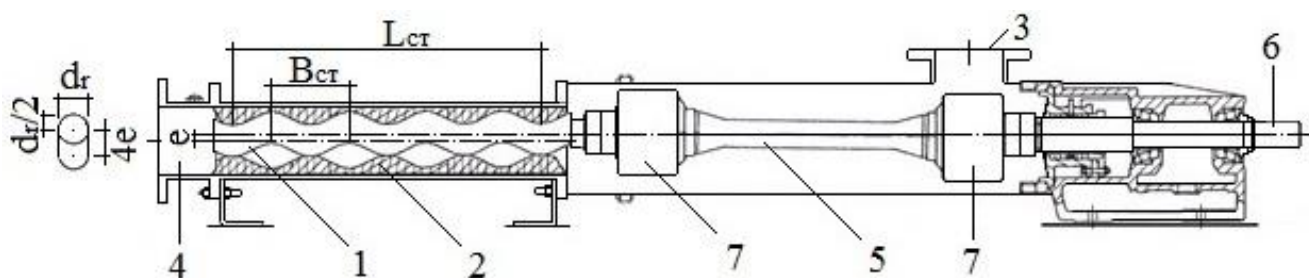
Конструкция ЭВН: 1- ротор, 2 – статор, 3 – загрузочный патрубок, 4 – выгрузной патрубок, 5 – карданный вал, 6 – вал, 7 – муфты.
